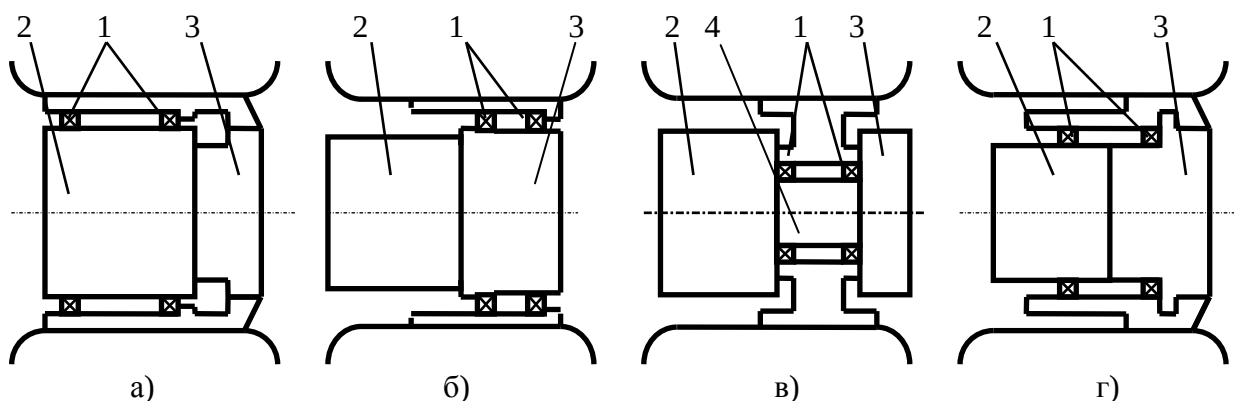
Схемы установки опорных подшипников колеса:
